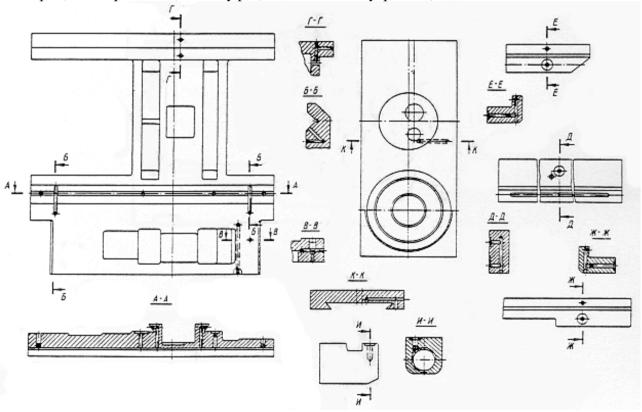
Схема расположения заглушек, пробок и прокладок в каретке.
